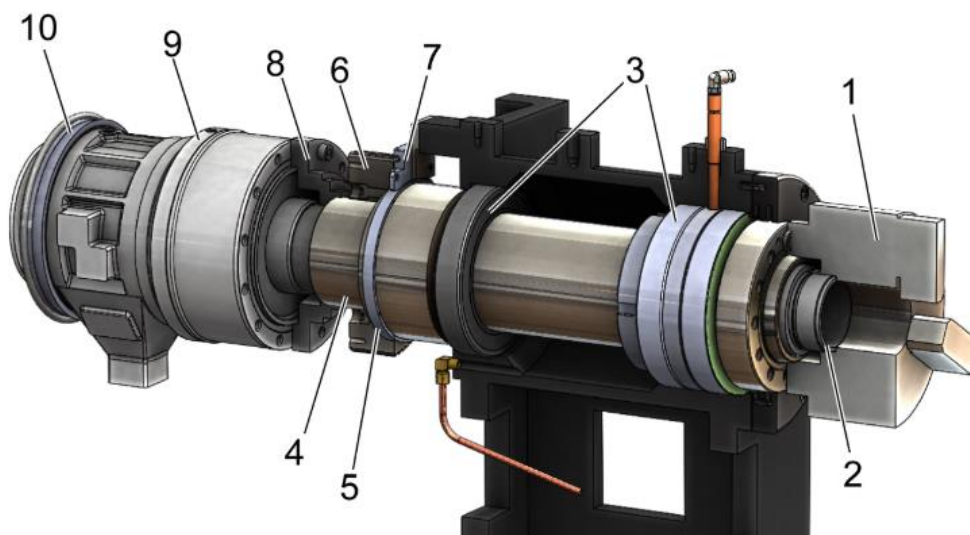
Класичний шпиндельний вузол із зубчастим приводом
